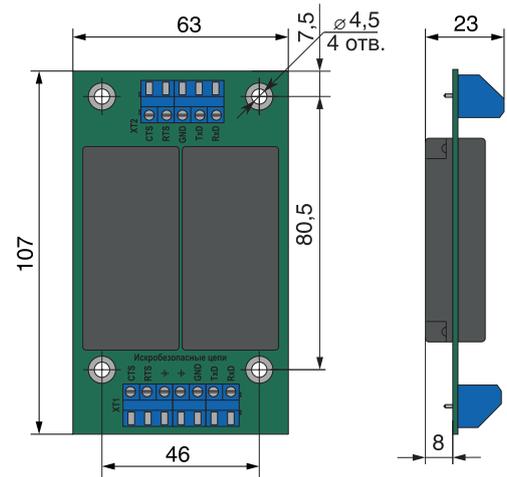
Габаритные размеры барьера ЭНИ-БИС-116-Ex-01
